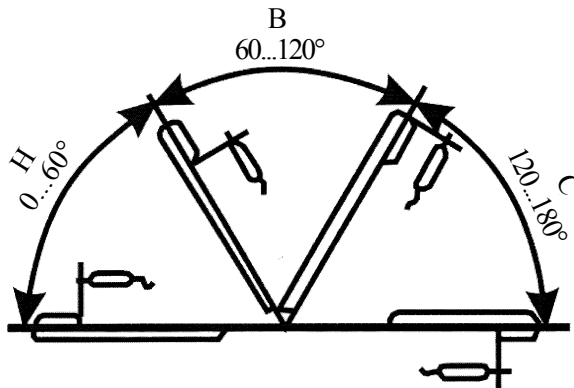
Схема просторового розташування швів при ручному дуговому зварюванні
